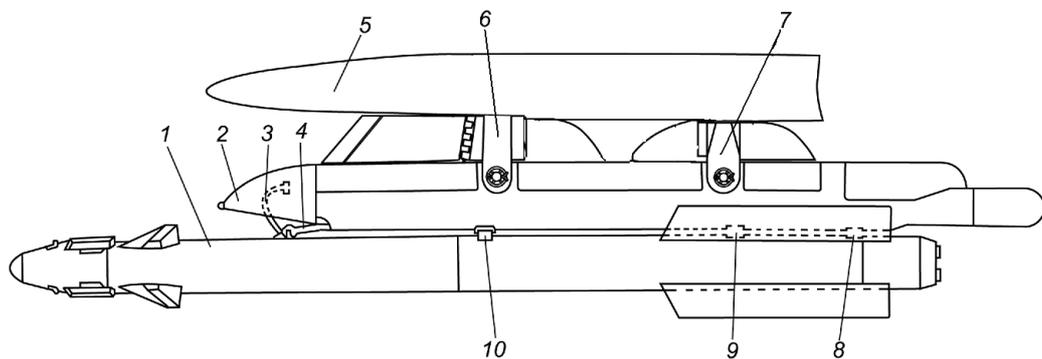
Установка АПУ П-72-1Д с ракетой на 1-6 точки подвески:
